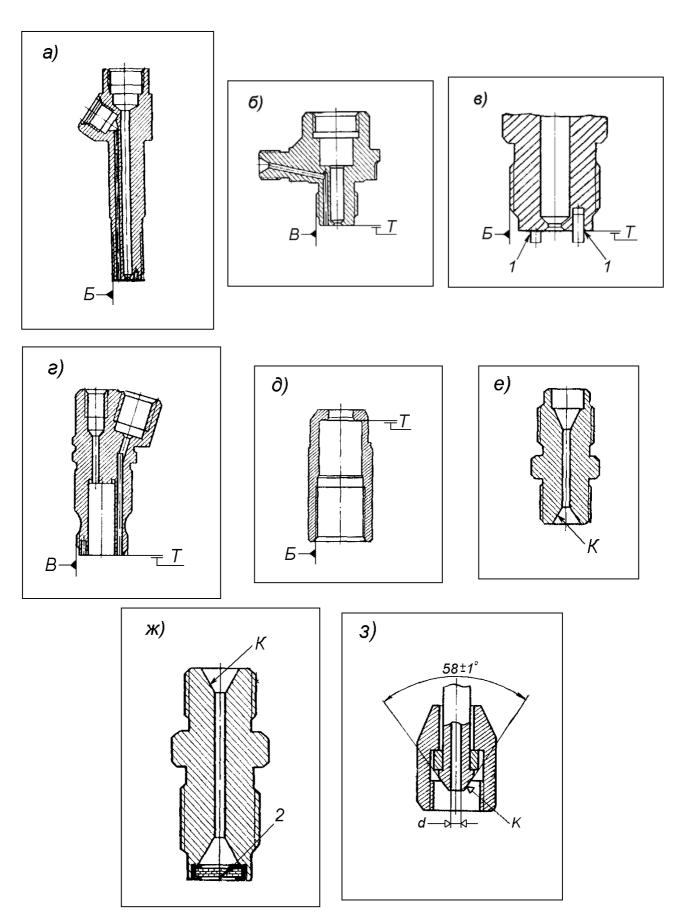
К контролю СЧ форсунок корпуса форсунки: а), б) — мод. 16; в) — мод. 26, 261, 262, 263, 181; г) — мод. 33, 19, 191; д) — гайки корпуса; е), ж) — штуцеров; з) — топливопровода высокого давления. Биение торца "Т" на диаметре относительно поверхности "Б" допускается не более 0,05 мм;  $d=2,0\pm0,15$  мм — сужение канала в зонах высадки конусов не допускается.
